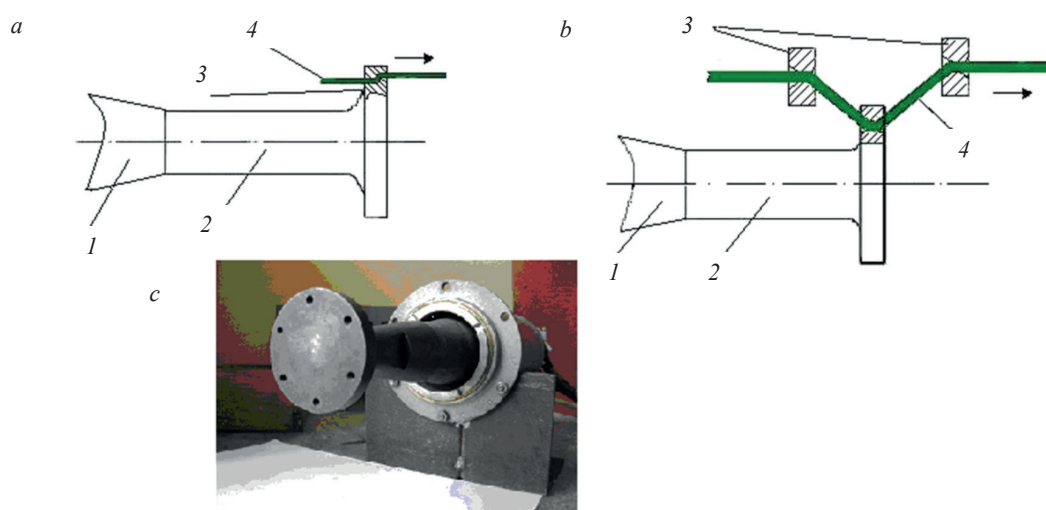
Схемы устройств РКУ протягивания проволоки с наложением ультразвуковых колебаний (a, b); вид концентратора колебаний с волочильными каналами (c)
